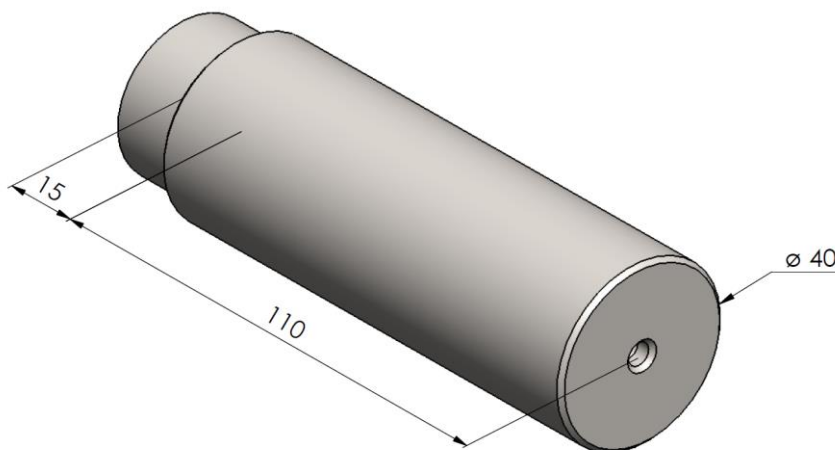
Detalhamento do corpo de prova com dimensões em mm.
